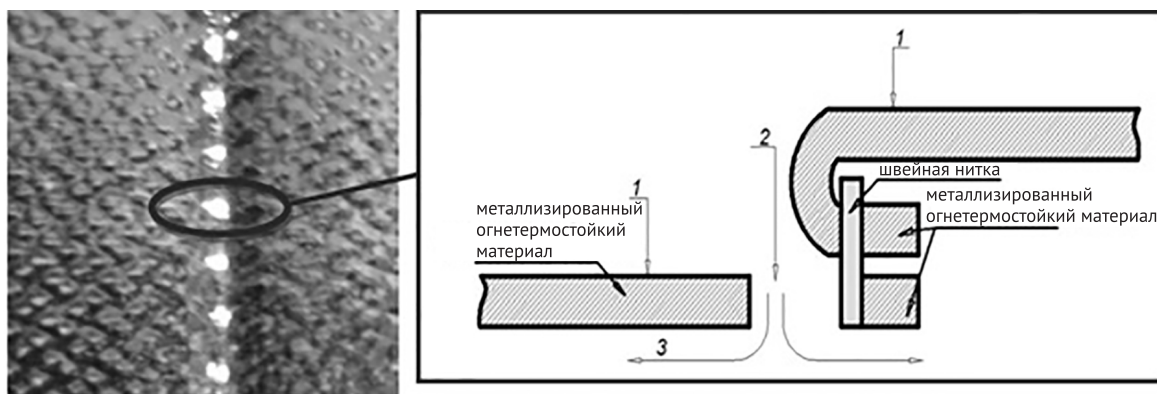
Внешний вид и структурная схема соединительного стачного шва в заутюжку, используемого для скрепления деталей ОСЗ ПТВ тяжёлого типа
